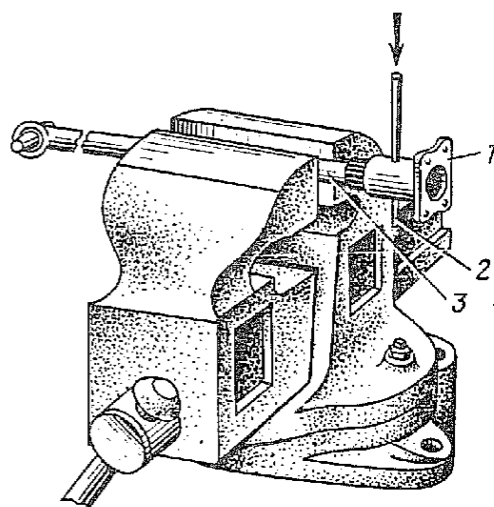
Выпрессовка стопорного штифта фланца полуоси:
